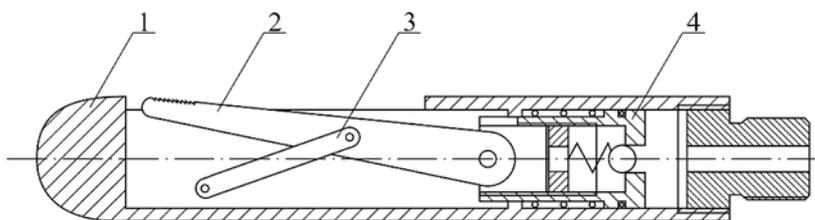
Схема щелеобразователя с рычажно-поворотным перемещением режущего органа: 1 – корпус; 2 – режущий орган; 3 – рычаг; 4 – поршень
